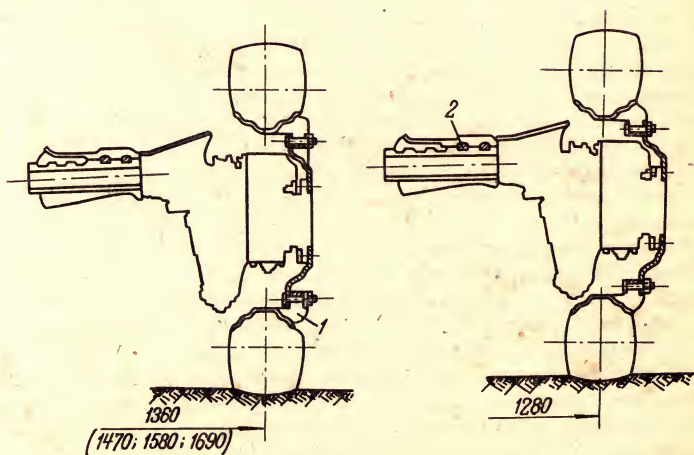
Регулировка колес передних колес трактора Т-40АМ:
